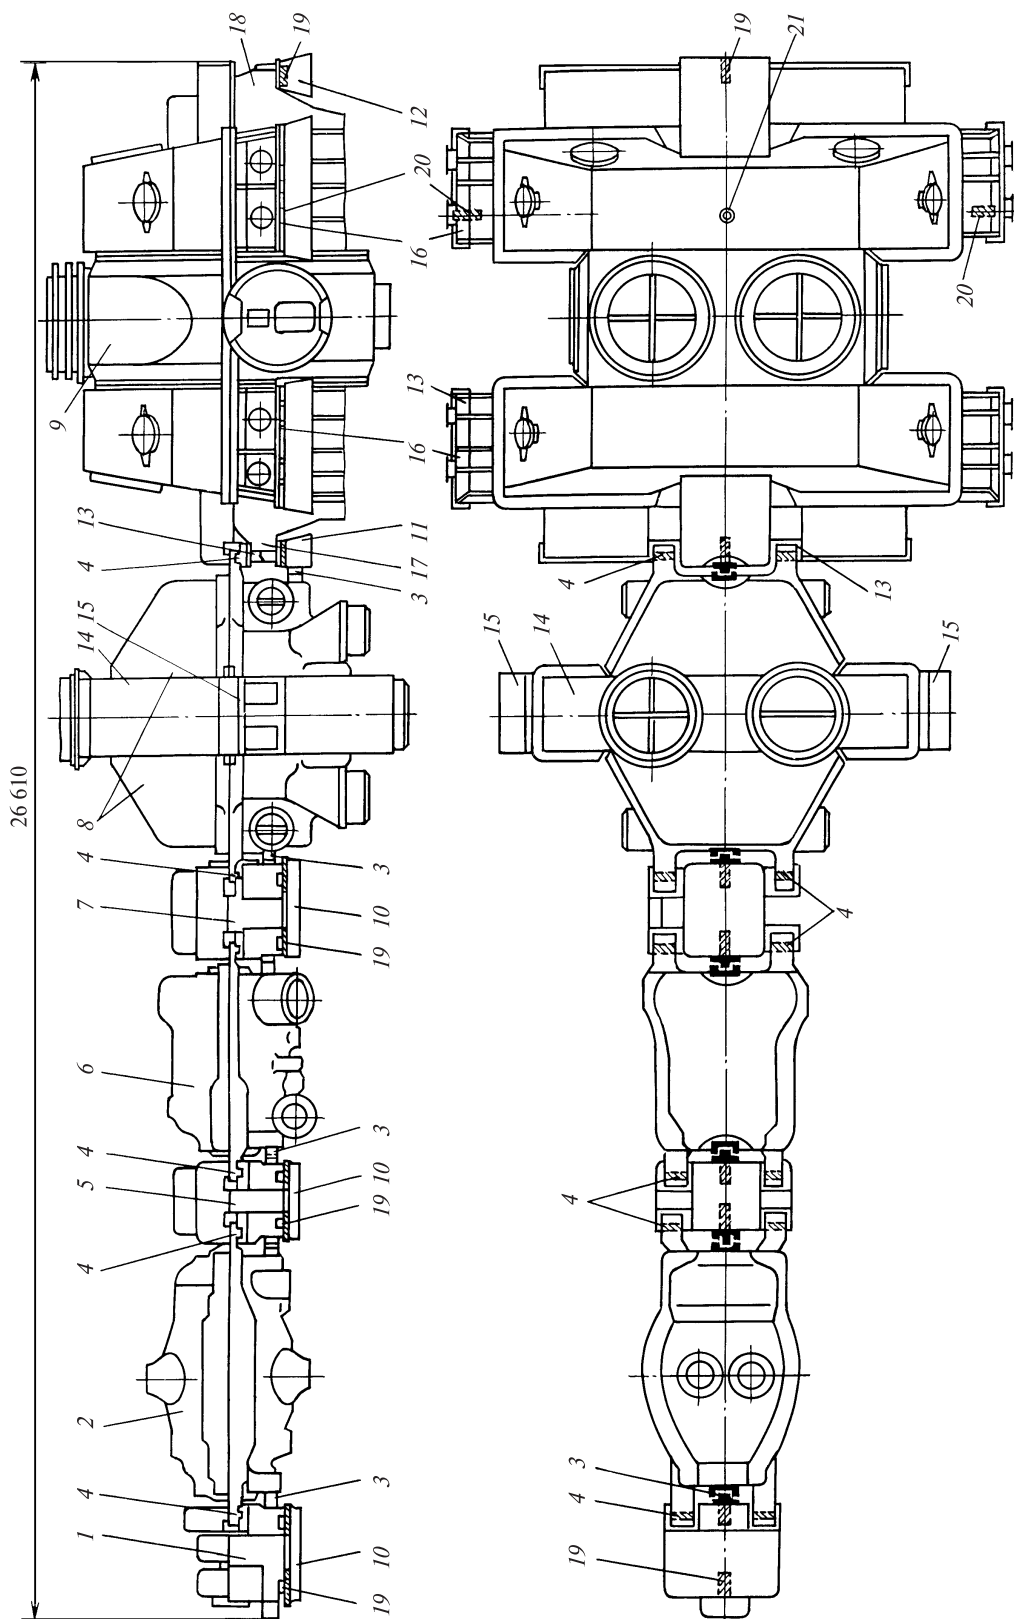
Опирание на фундамент турбины Т-250/300-23,5 ТМЗ
